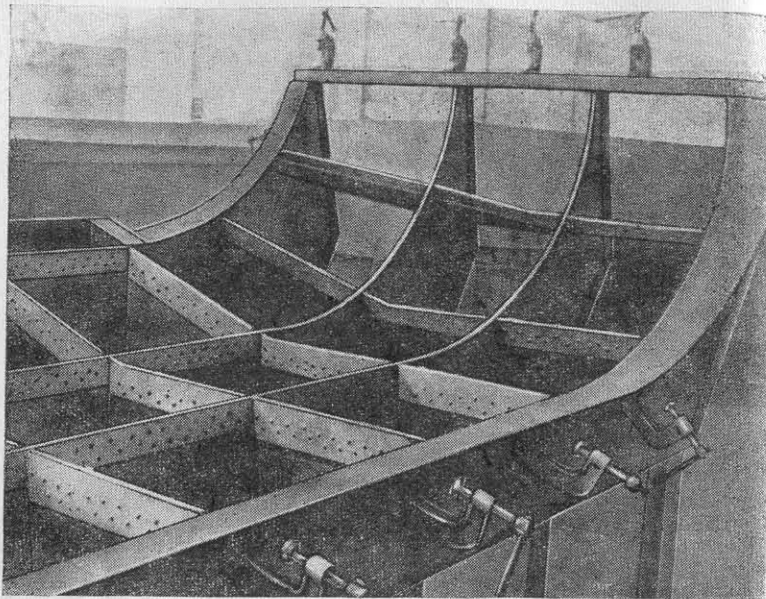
Постель для сборки и сварки полубъемных секций с прижимными струбцинами.
